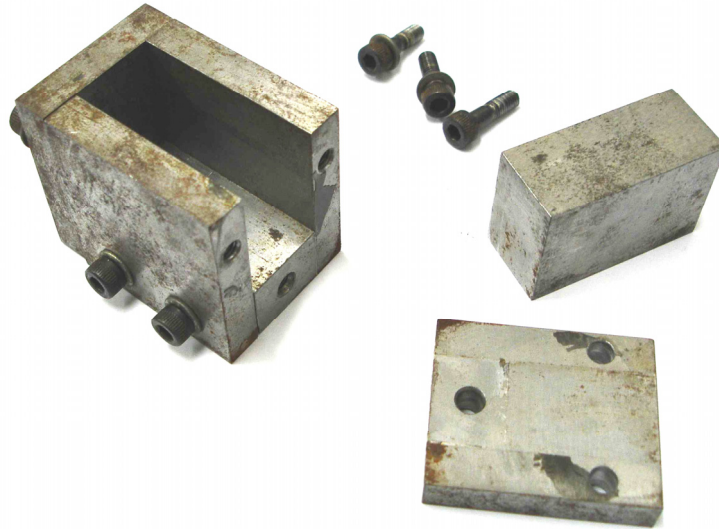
Aparato utilizado para moldar a camada de retaguarda.
